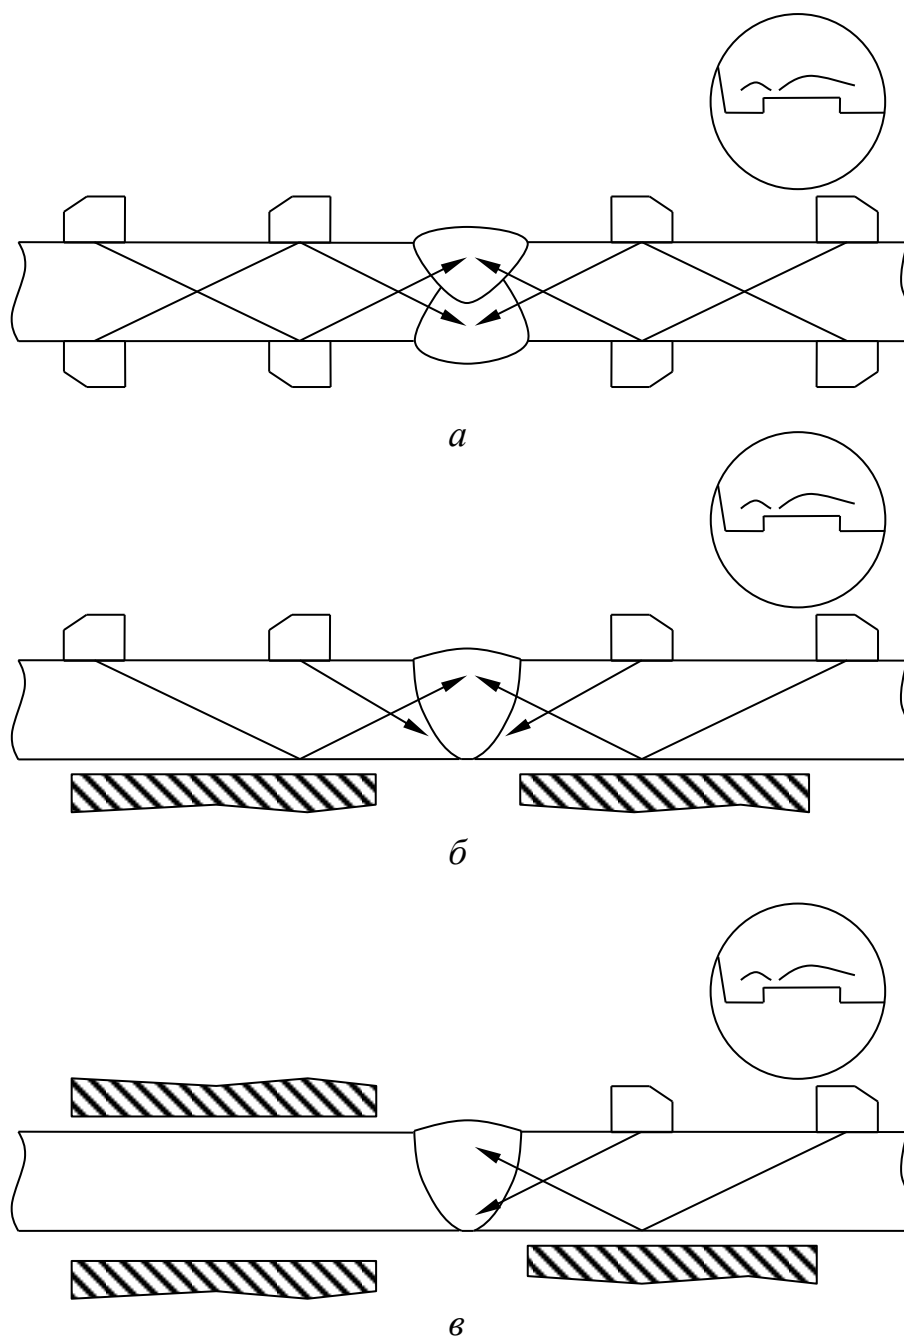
Схемы контроля стыковых сварных соединений
